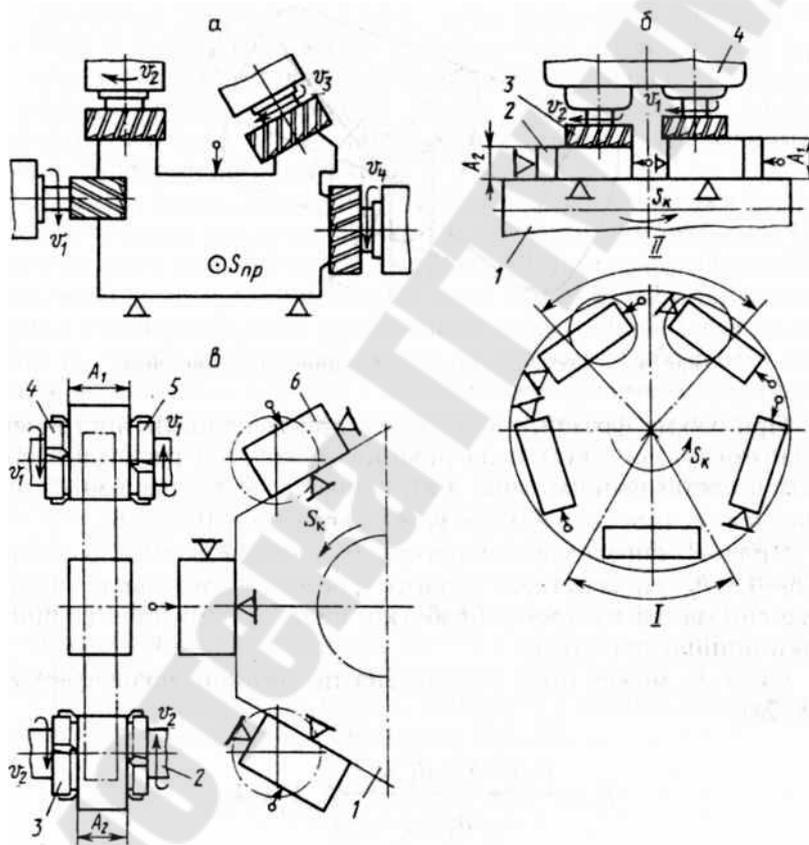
Схемы обработки фрезерованием на продольно-фрезерном (а), карусельно-фрезерном (б) и барабанно-фрезерном (в) станках
